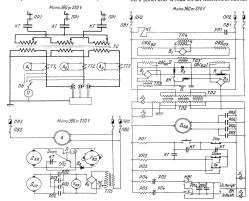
Принципиальная электриче Fig. 6. A-372 Welding Apparatus electrical connections diagram
